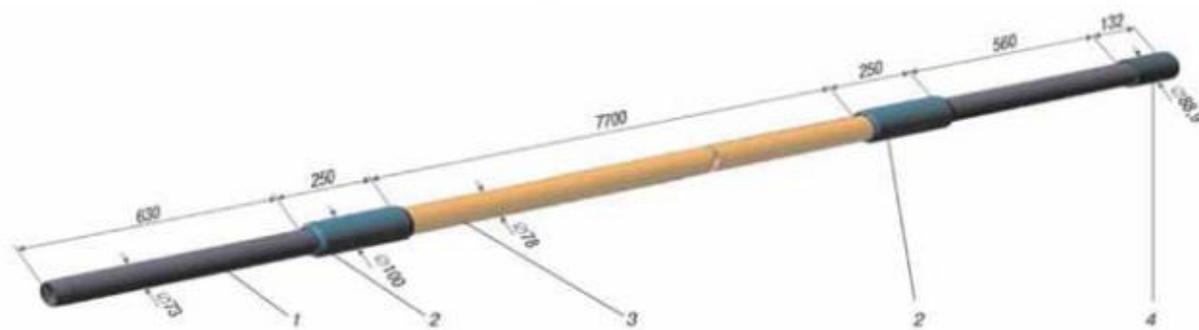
Стеклопластиковая труба со стальными удлинителями
